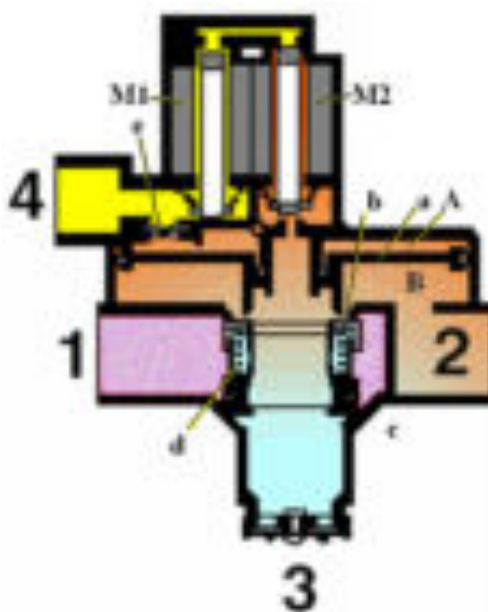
Фаза сброса давления из тормозной камеры заблокированного колеса.
